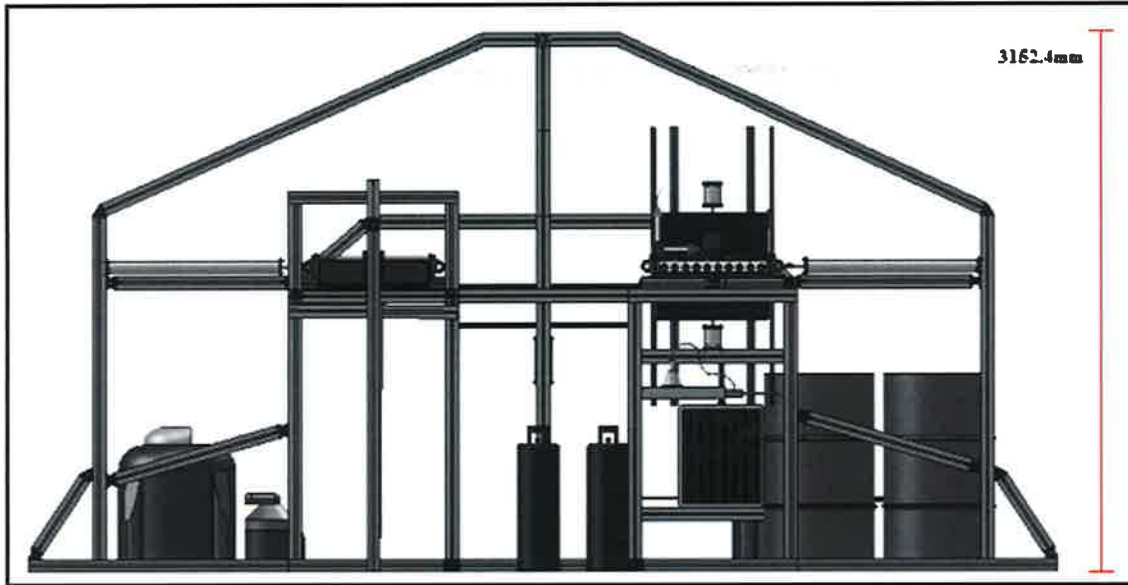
Dimensiones de máquina NTC terminada, vista frontal
